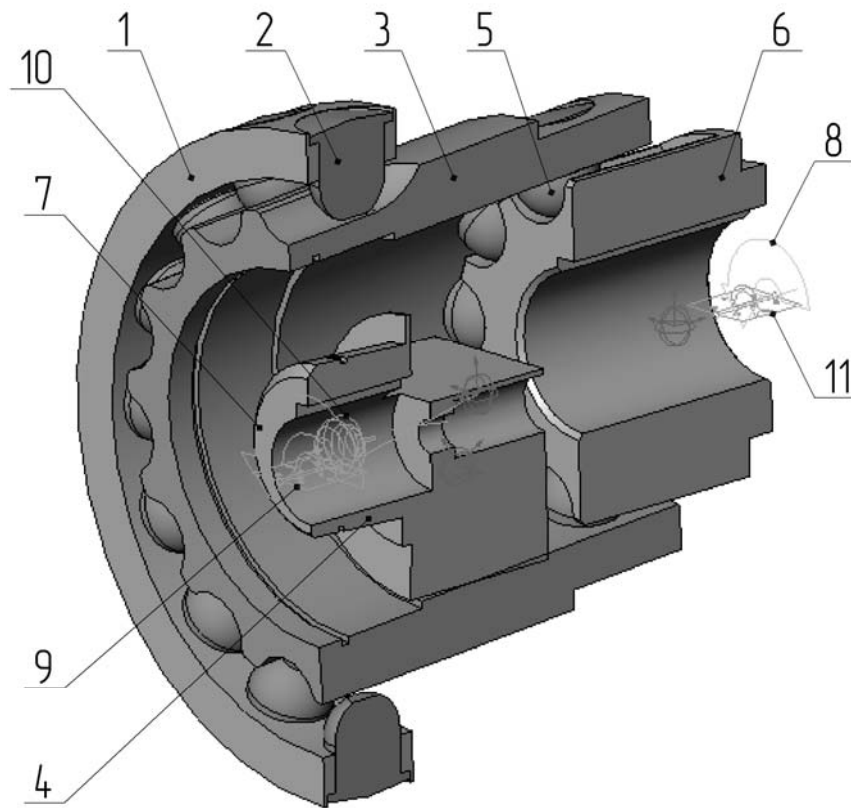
Компьютерная модель прецессионного редуктирующего механизма: 1 – корпус; 2, 5 – сферический палец; 3 – сателлит; 4 – кривошип; 6 – угловая муфта; 7 – крутящий момент; 8 – нагружающий момент; 9 – подшипник входного вала; 10 – сферический подшипник; 11 – подшипник выходного вала
